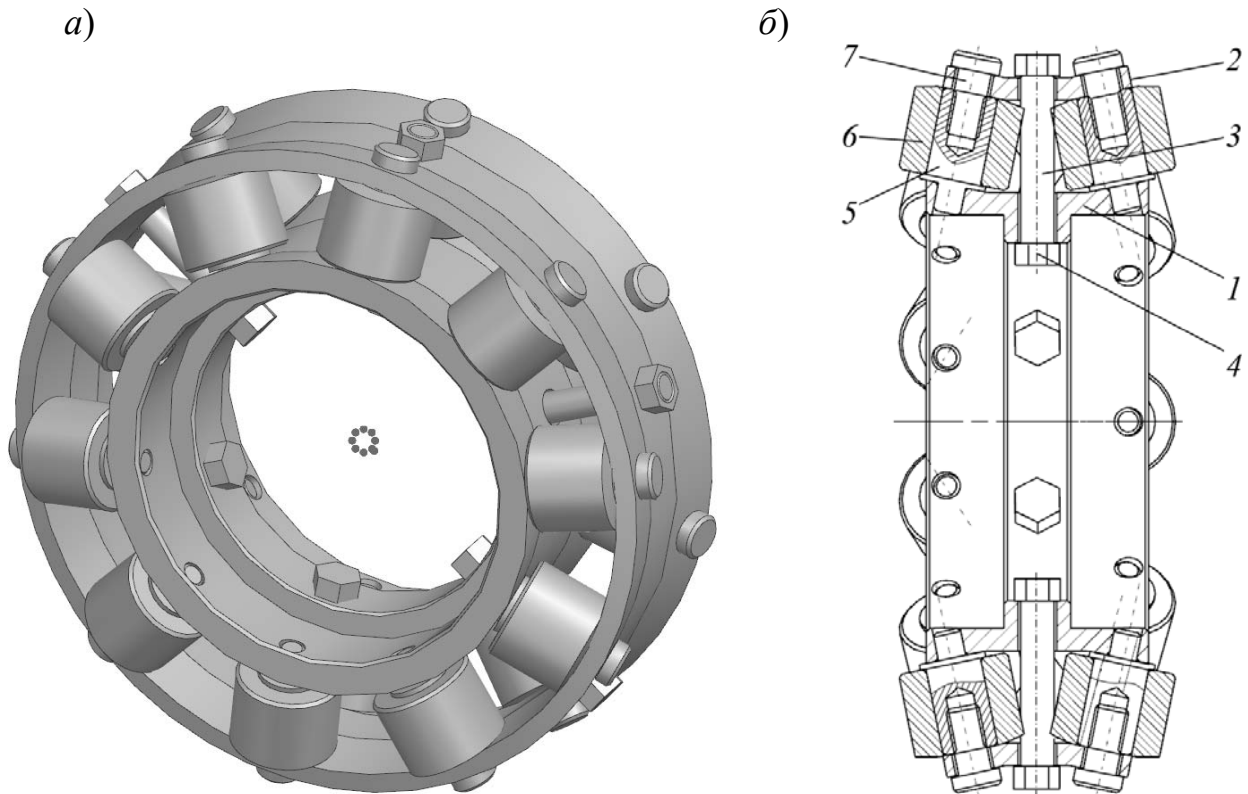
Сборный сателлит СРП: *a* – модель; *б* – конструктивная схема; 1 – основание; 2 – наружное кольцо; 3 – несущий болт; 4 – гайка; 5 – стержень; 6 – ролики; 7 – стержневой винт
